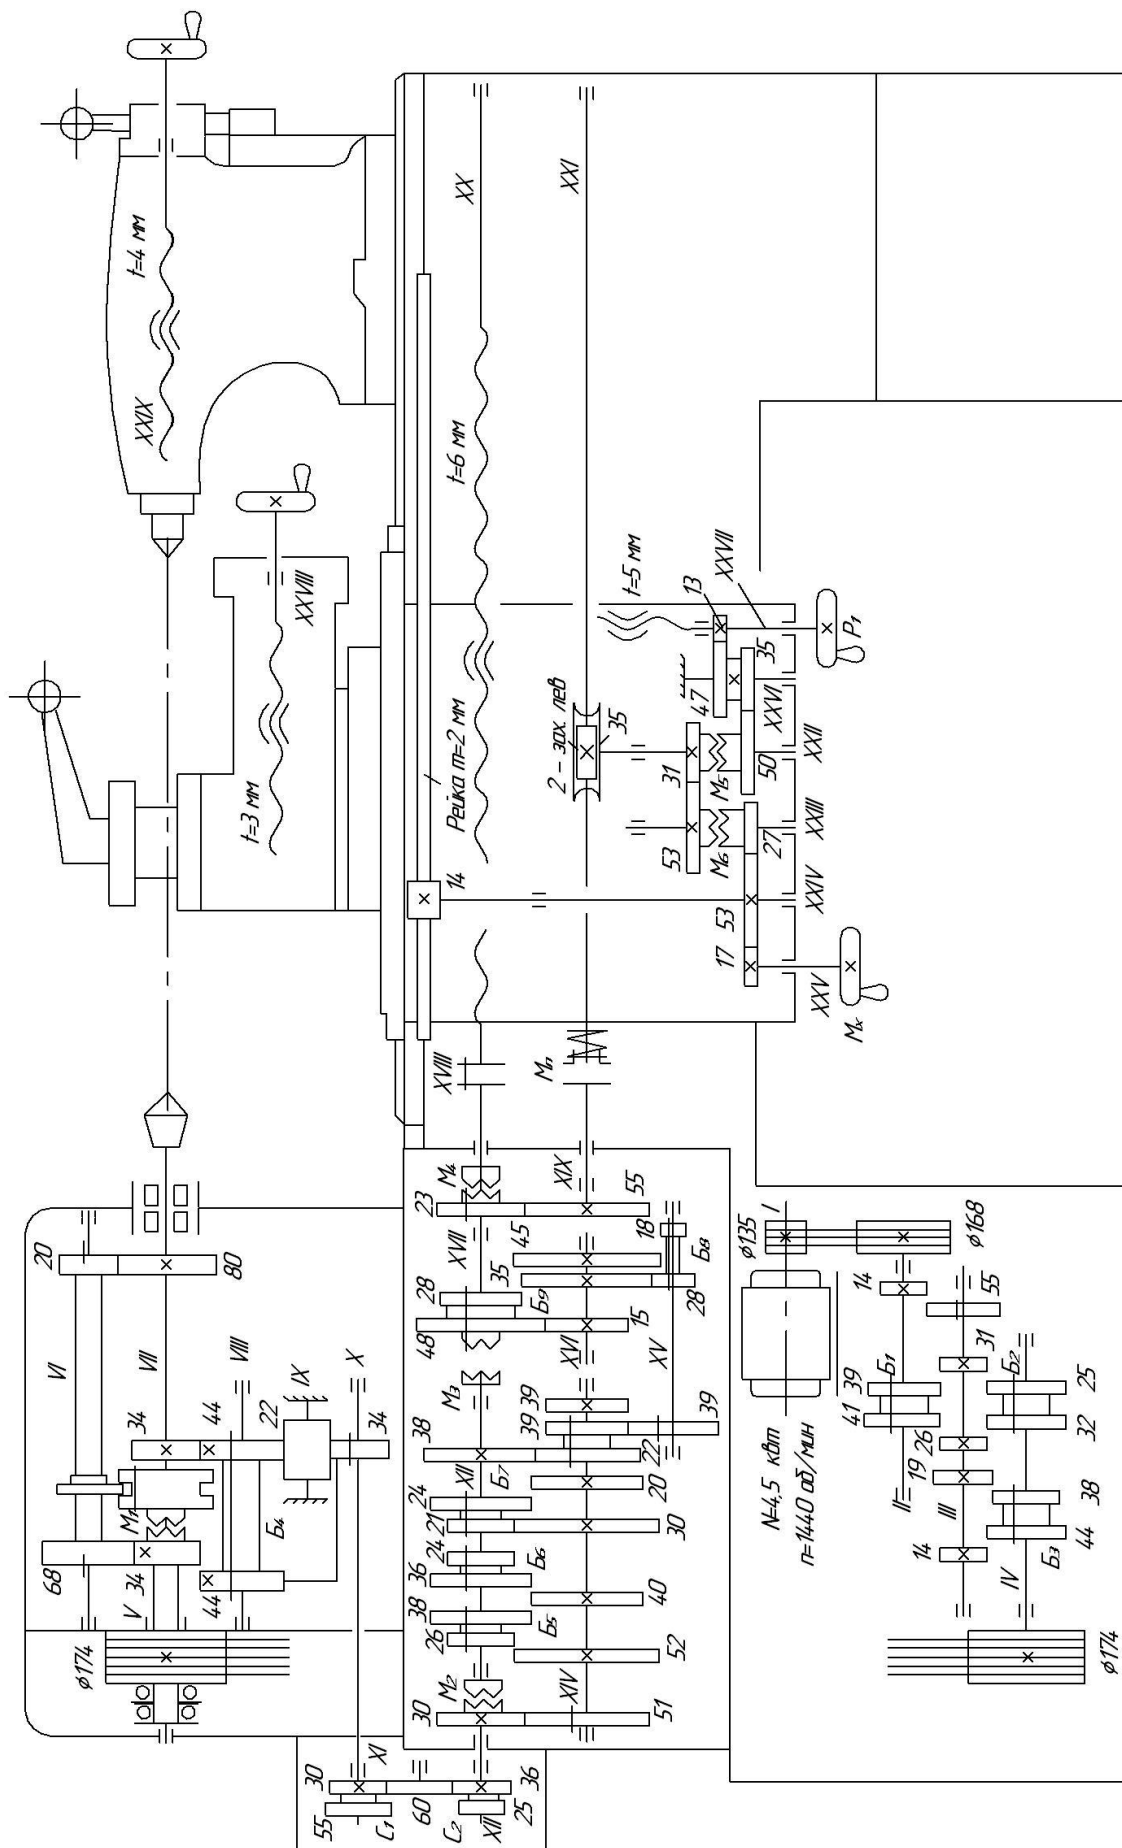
Кинематическая схема токарно-винторезного станка 1А616
